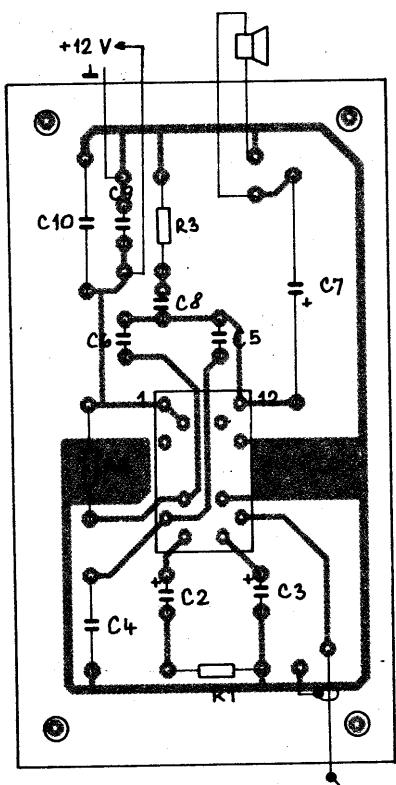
Rozložení součástek na desce se spoji z obr. 94
